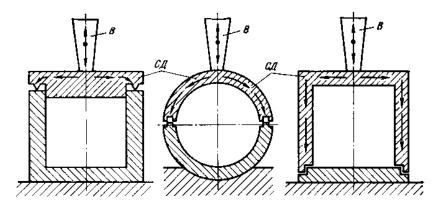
Схема передаточной ультразвуковой сварки: В – волновод; СД – свариваемые детали.
